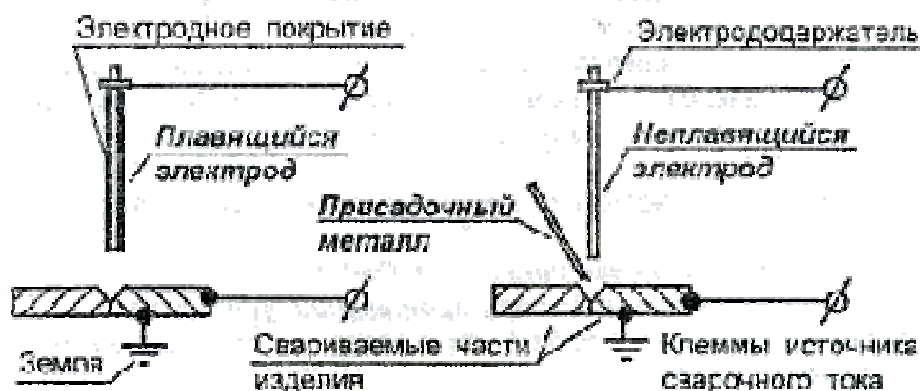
Сварка плавающимся и неплавающимся электродом
